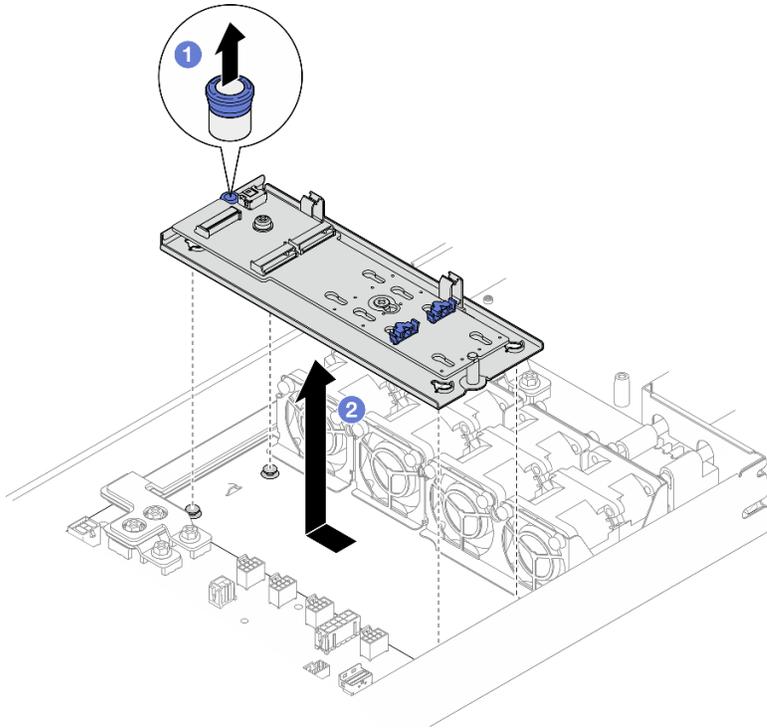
Entfernen des M.2-Bootadapterrahmens
